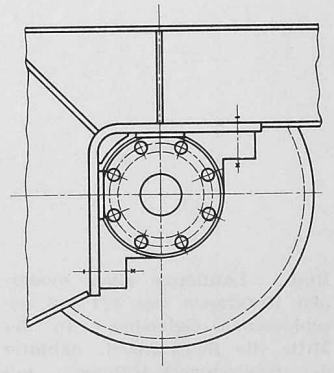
Ecklager einer Kranlaufrolle neuer Bauweise
